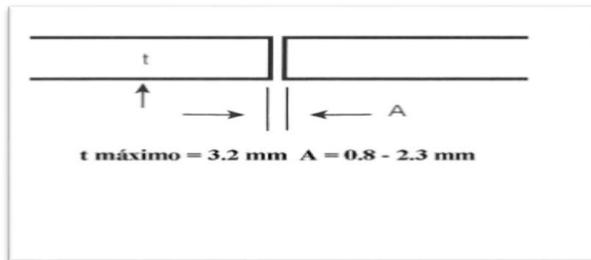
Junta para soldadura a tope de etapas.
